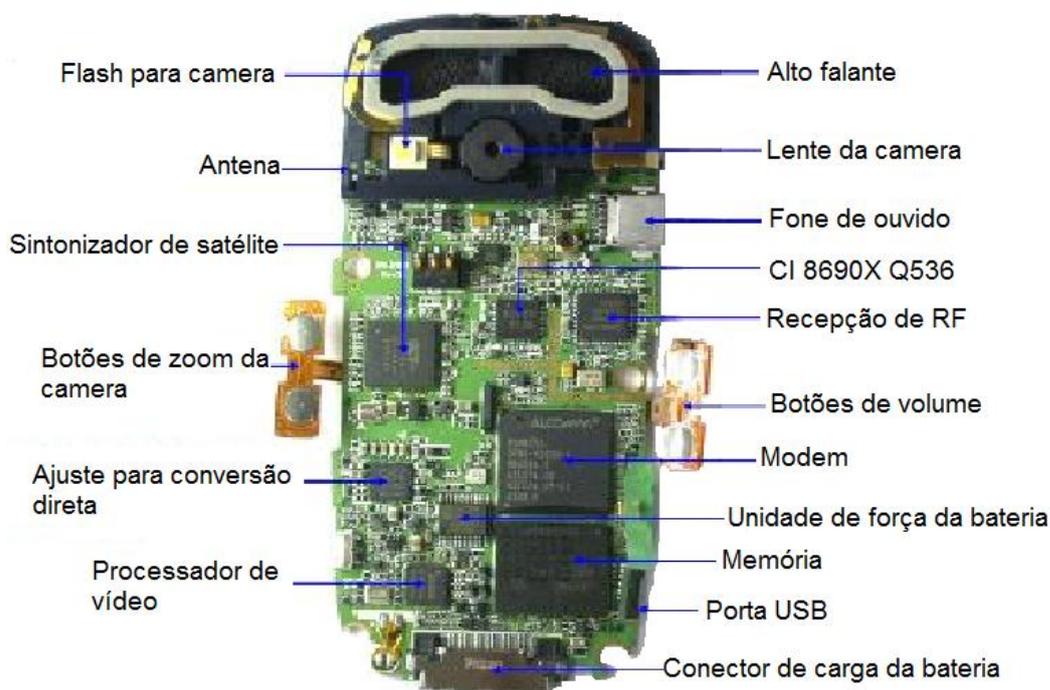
Placa de circuito impresso de um telefone celular de segunda geração e seus componentes
